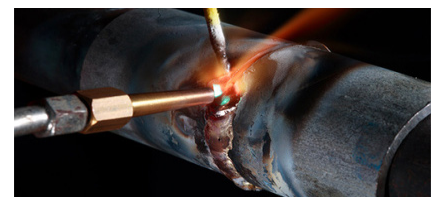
Unión de dos piezas mediante soldadura.
